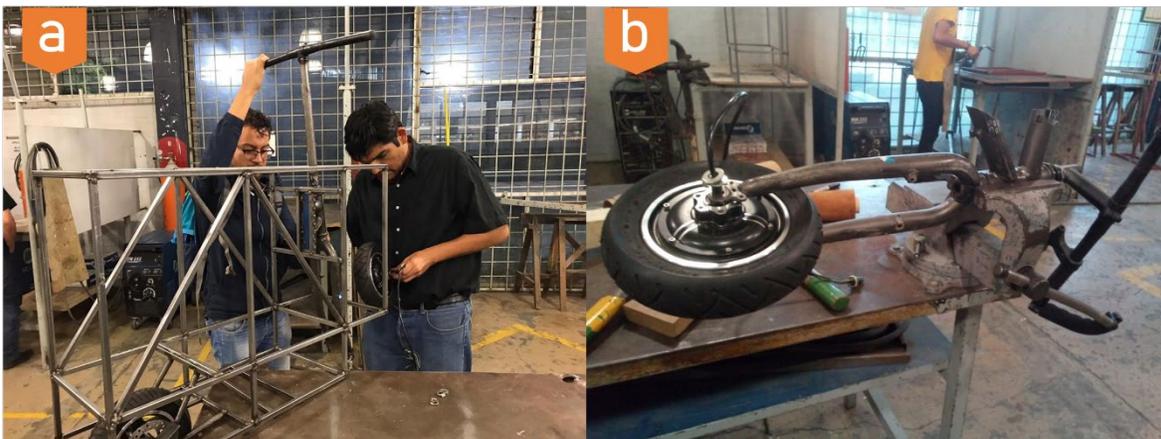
a) Manufactura estructura VUMi, b) Manufactura horquilla de dirección VUMi.
